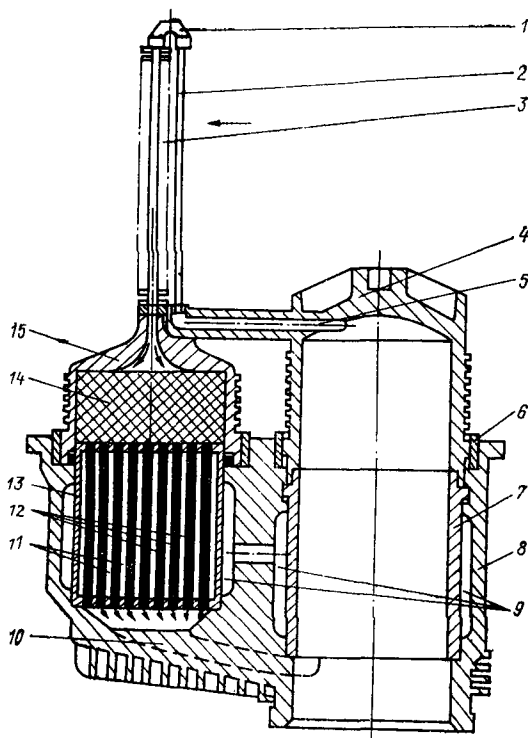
Эволюция конструкции нагревателя двигателей фирмы Филипс Глоеилампен фабрикен.
